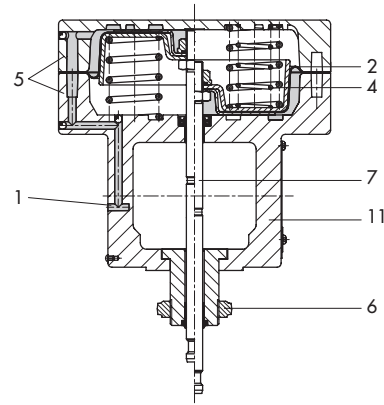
· Tipo 3277-5 para montaje directo de accesorios
